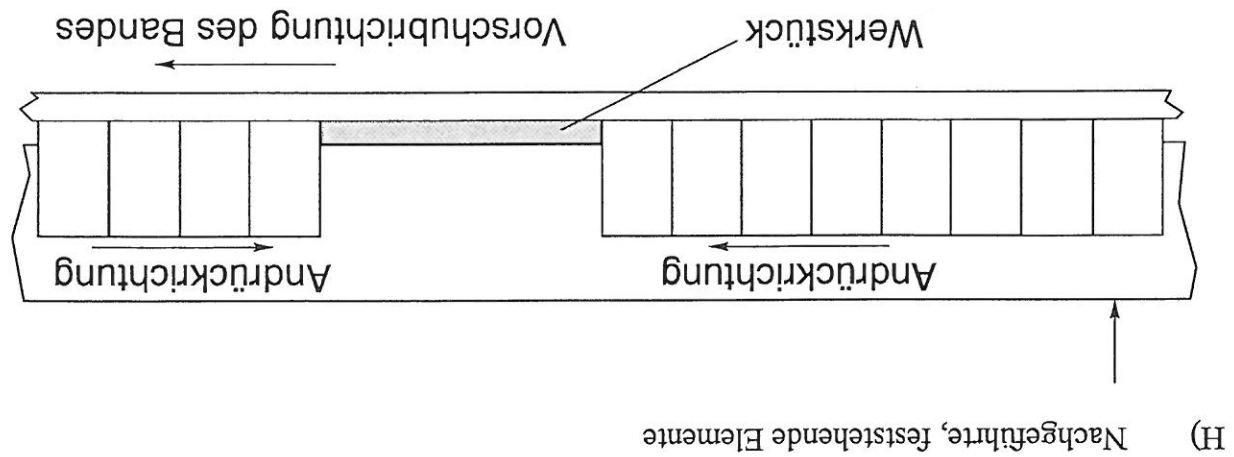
Nachgeführte, feststehende Elemente
